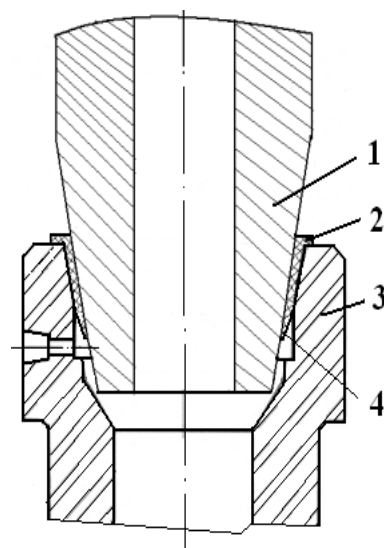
Модернизированное устройство для защиты струи металла при разливке на МНЛЗ:
